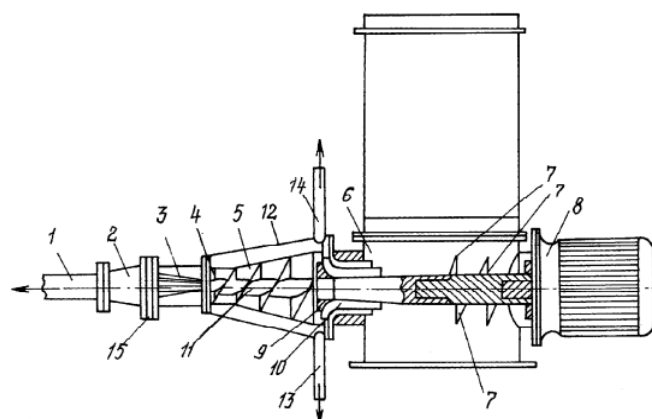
Устройство для обработки и транспортировки волокнистой массы:
